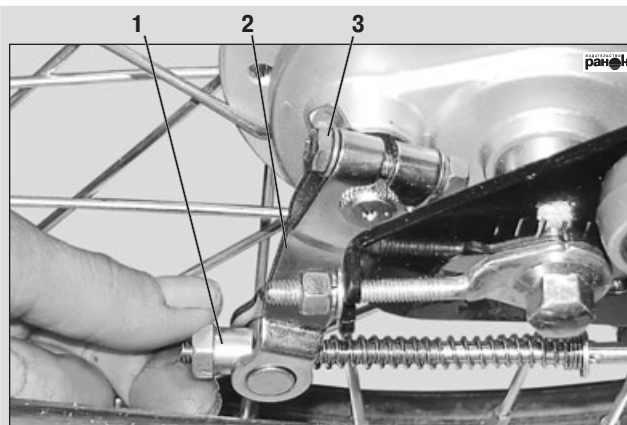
Регулировка заднего тормоза: 1 — регулировочная гайка; 2 — тормозной рычаг; 3 — гайка тормозного рычага заднего колеса
